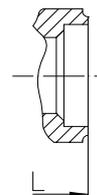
3 / 632...3 mit Schweißmuffen
